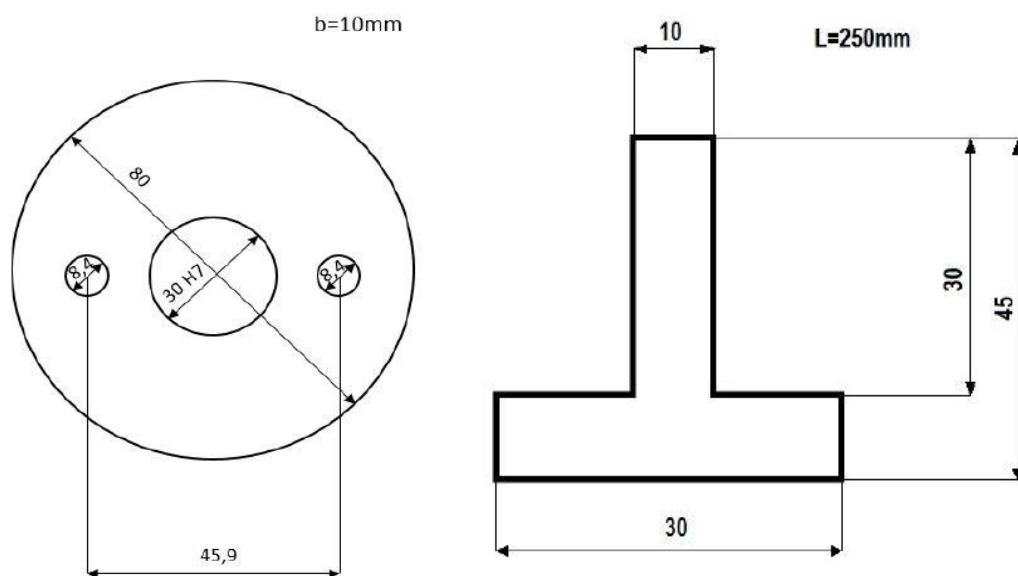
Dimensiones (mm) de las piezas a ensayar protocolo industrial.
